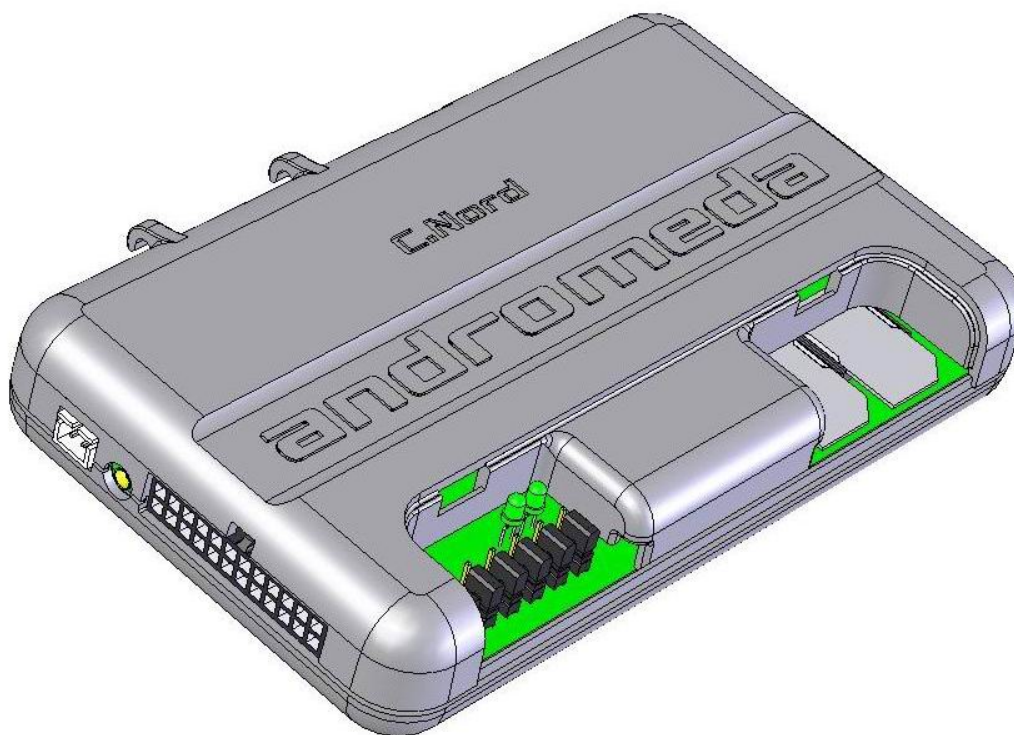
Блок МБ – 04 в пластмассовом корпусе без боковой съемной крышки
